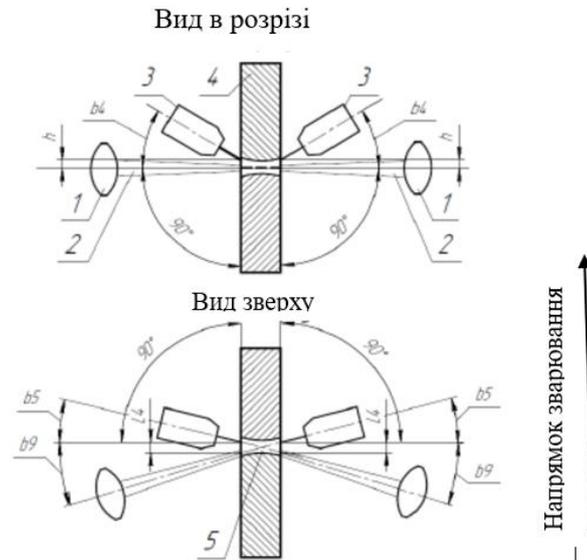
Схема ГЛДЗ, метод «Гібрид двосторонній» зварного стикового з'єднання в горизонтальному положенні (РС):
